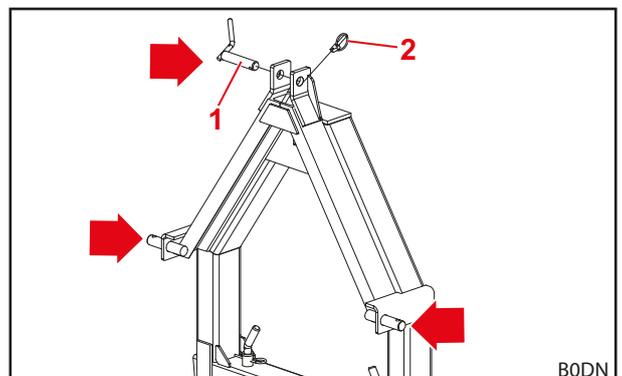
Punti di fissaggio per il montaggio sul lato posteriore del trattore
